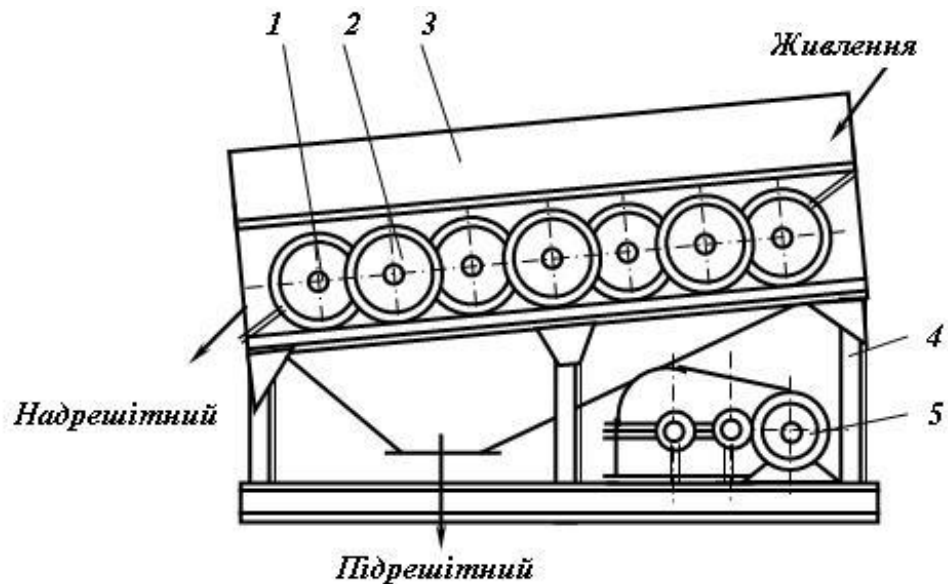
Валковий грохот: 1 - валки; 2 – диски; 3 - короб грохота; 4 - рама; 5 - привод
